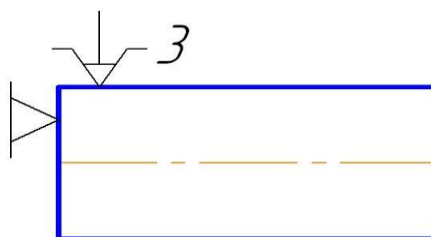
Умовна схема базування при обробці на токарних верстатах
